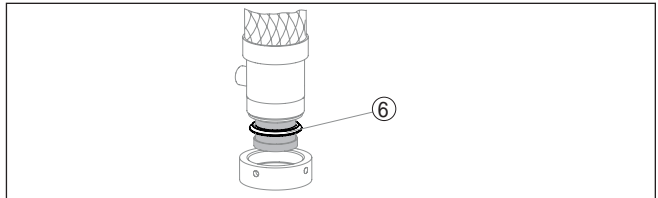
Montage-Kit - Szintillator-Kühlschlauch - unten
